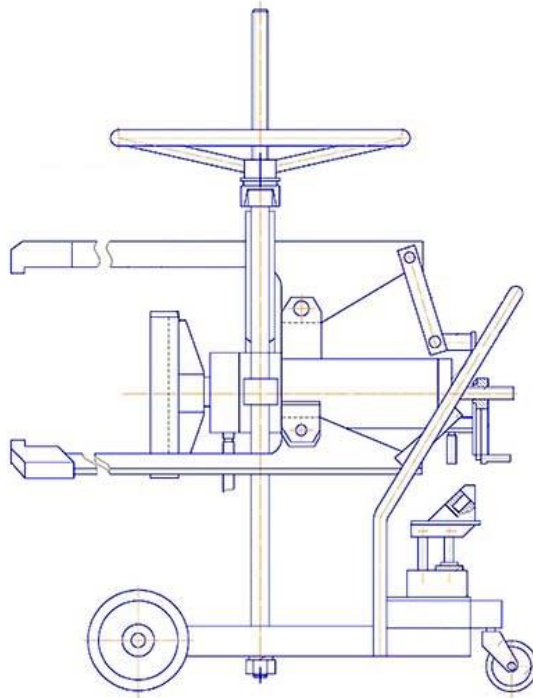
Загальний вигляд станда (вигляд збоку)
